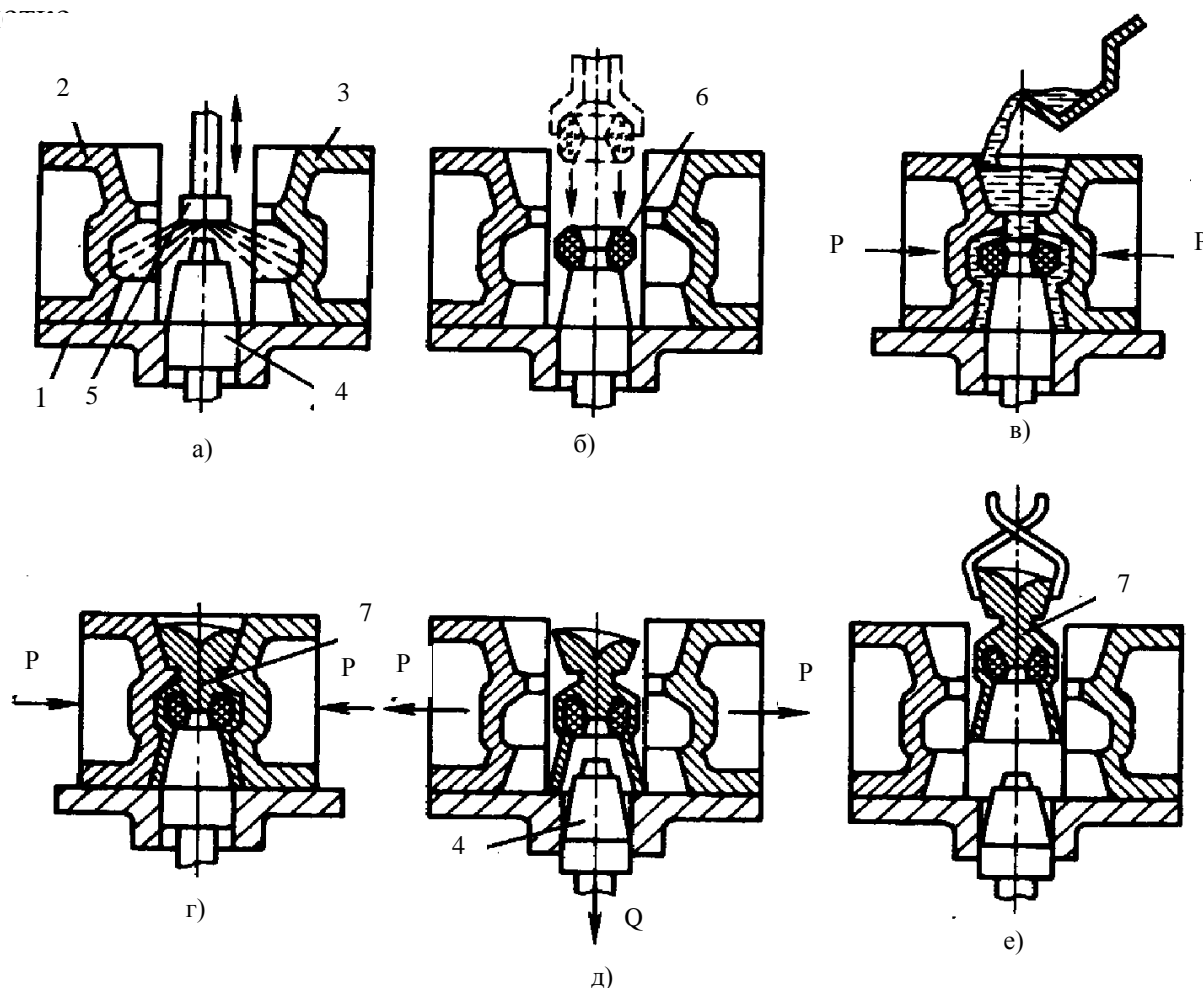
Схема операций при заливке в кокиль. 1 – поддон; 2,3 – симметричные полуформы; 4 – металлический стержень; 5 – пульверизатор; 6 – песчаный стержень; 7 – отливка
